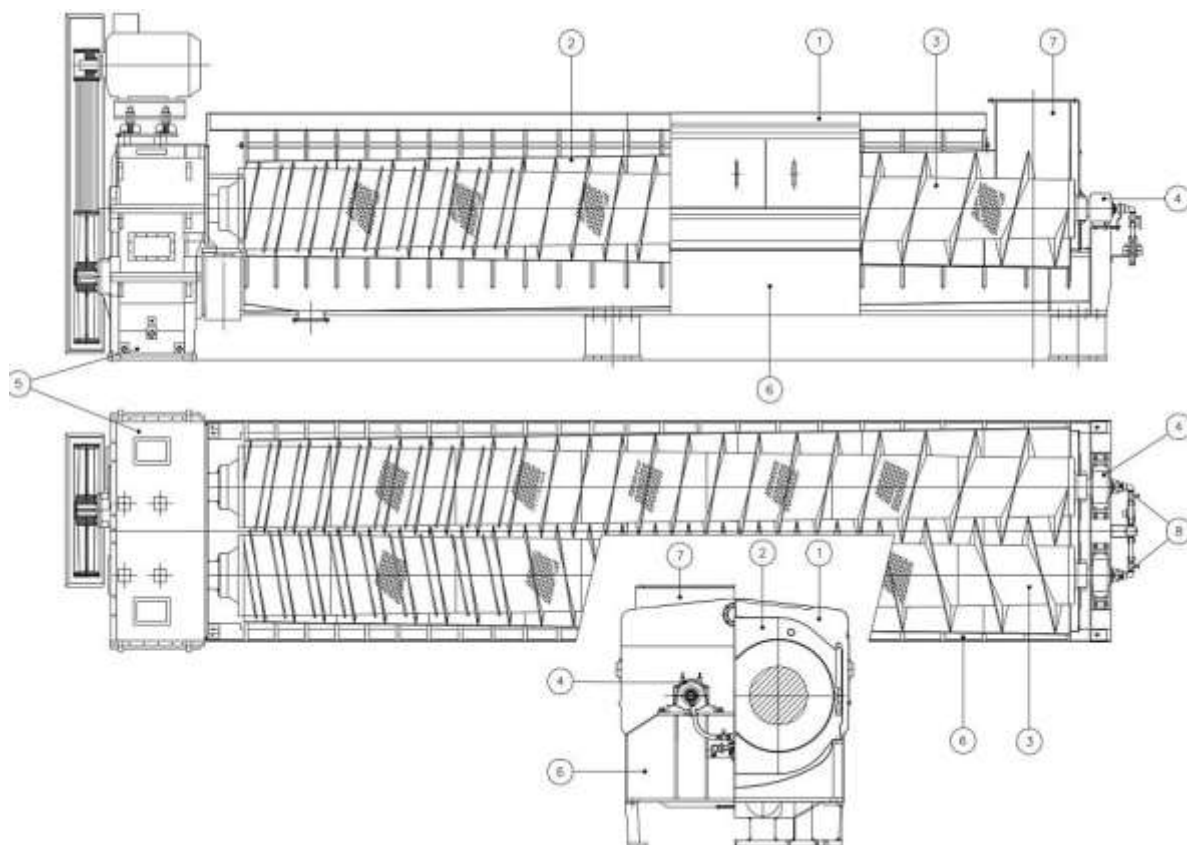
Пресс глубокого отжима жом: 1 – корпус; 2 – фильтрующий узел; 3 – фильтрующий узел; 4 – опоры валов; 5 – редуктор; 6 – загрузочный бункер; 7 – система промыва валов
